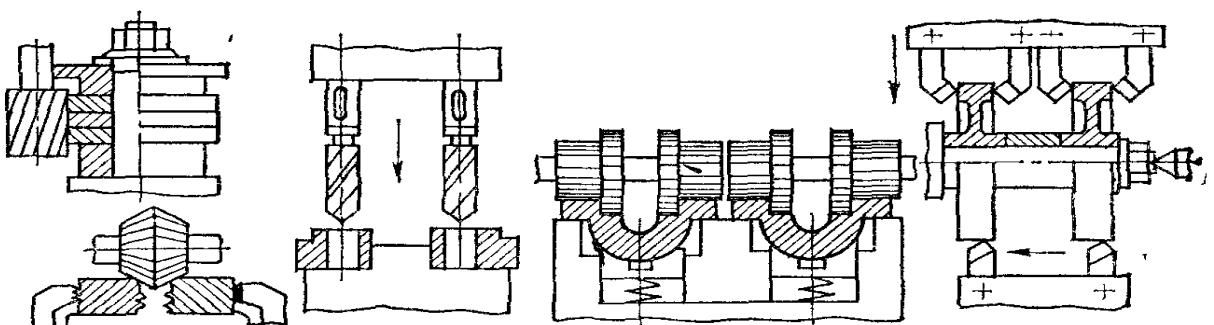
Схеми багатомісної паралельної багатоінструментної обробки з одночасним встановленням заготовок
